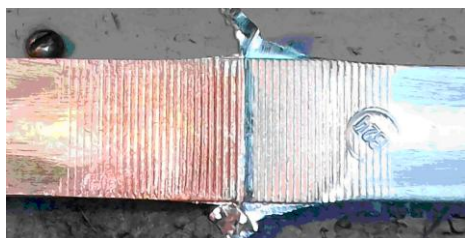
Сварное соединение Cu-Al
